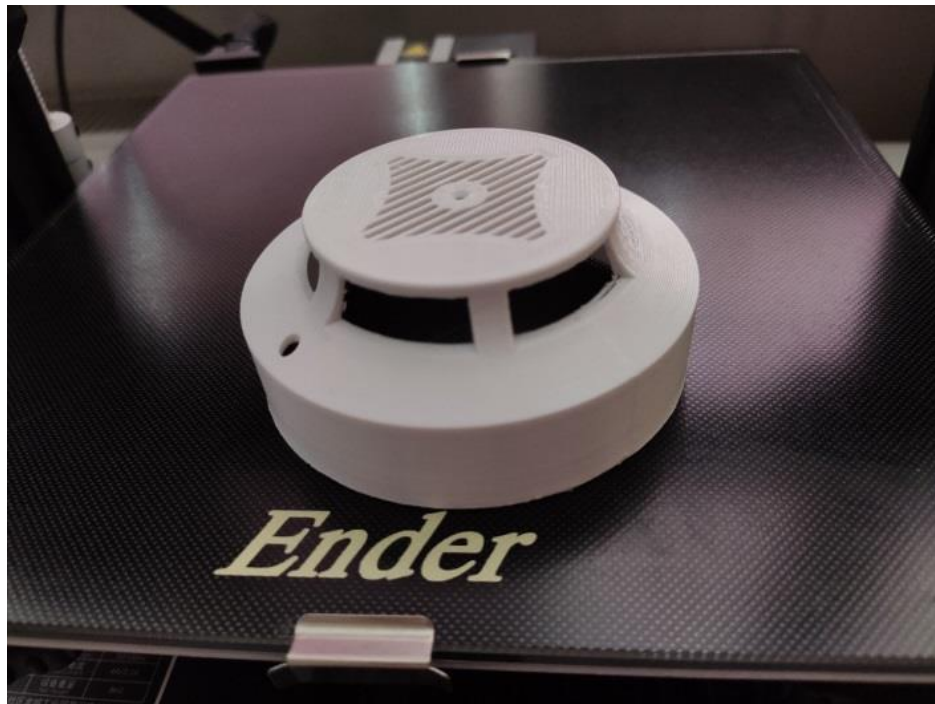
Зовнішній вигляд прототипу зовнішньої частини корпусу детектора диму
